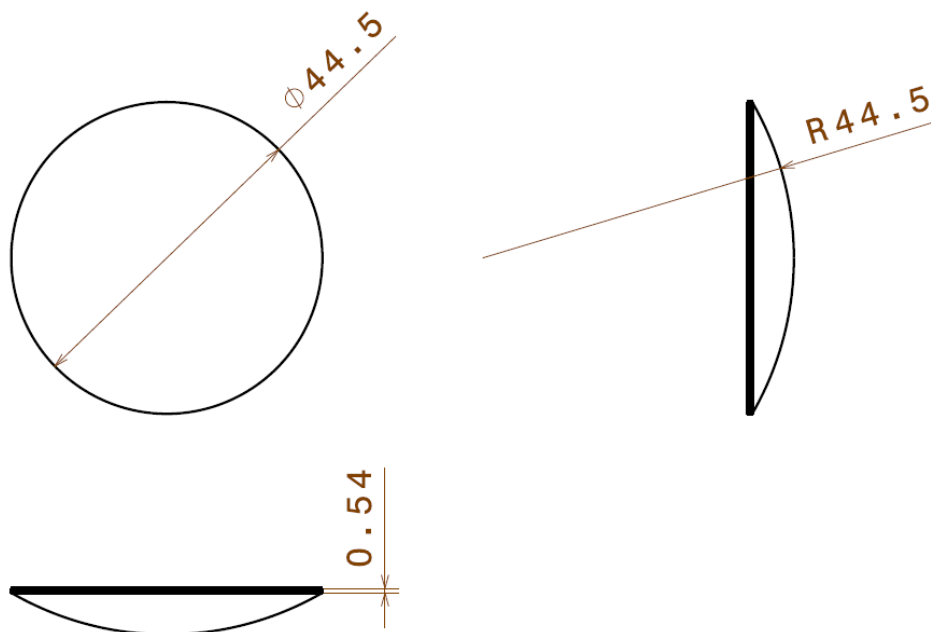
Plano con alzado (arriba, izquierda), planta (abajo) y perfil (arriba, derecha) del transductor PZ52
